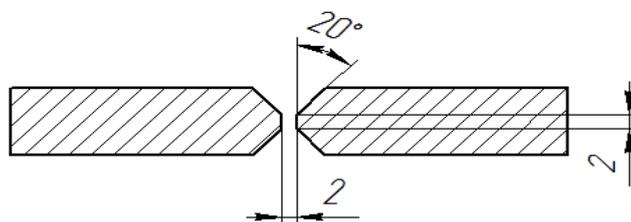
Разделка кромок для электродуговой сварки
